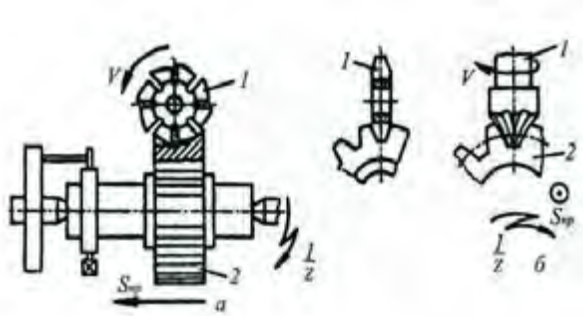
Схеми фрезерування зубців за методом копіювання
